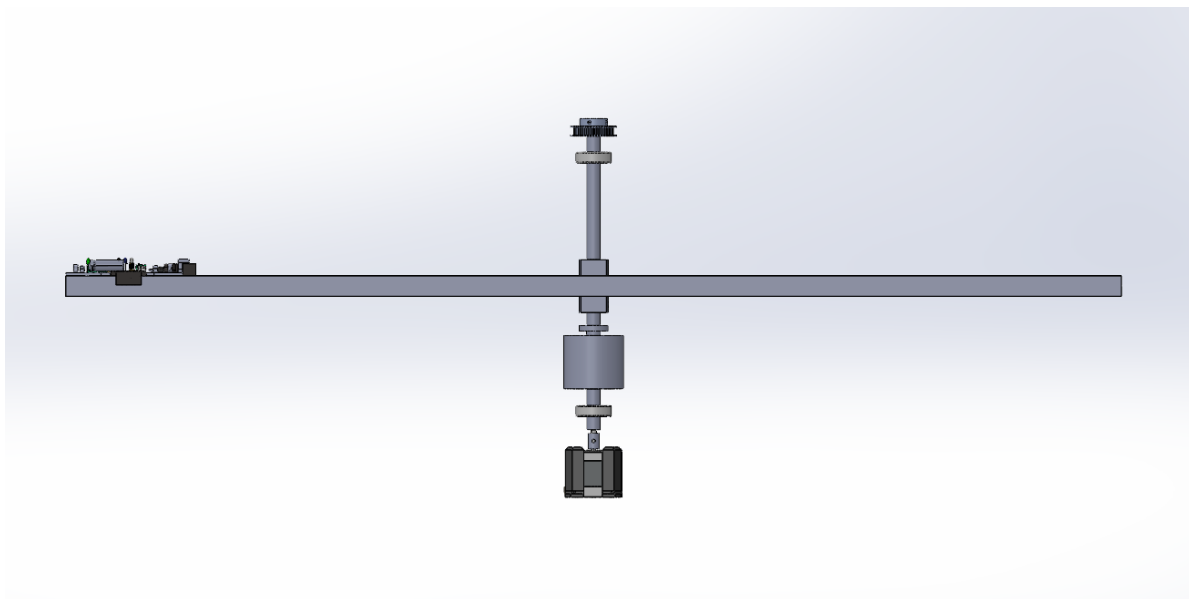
3D модель, обертова частина з валом, підшипниками та двигуном.
